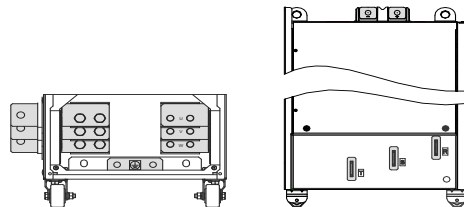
Расположение клемм главной цепи конструкций T7 - T9
